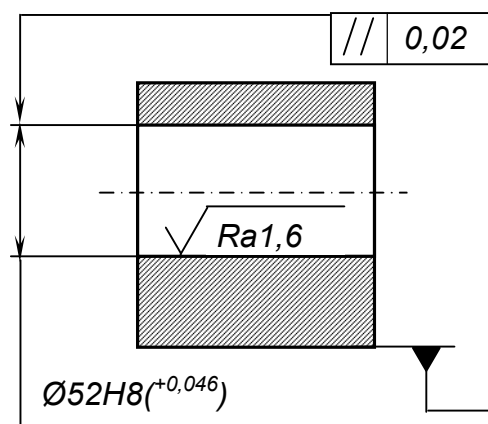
Ескіз до прикладу визначення кількості ступенів обробки отвору в заготовці деталі типу «корпус»
